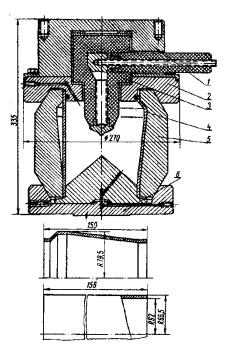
Оснастка для электрогидравлической штамповки деталей из цилиндрической заготовоки:
